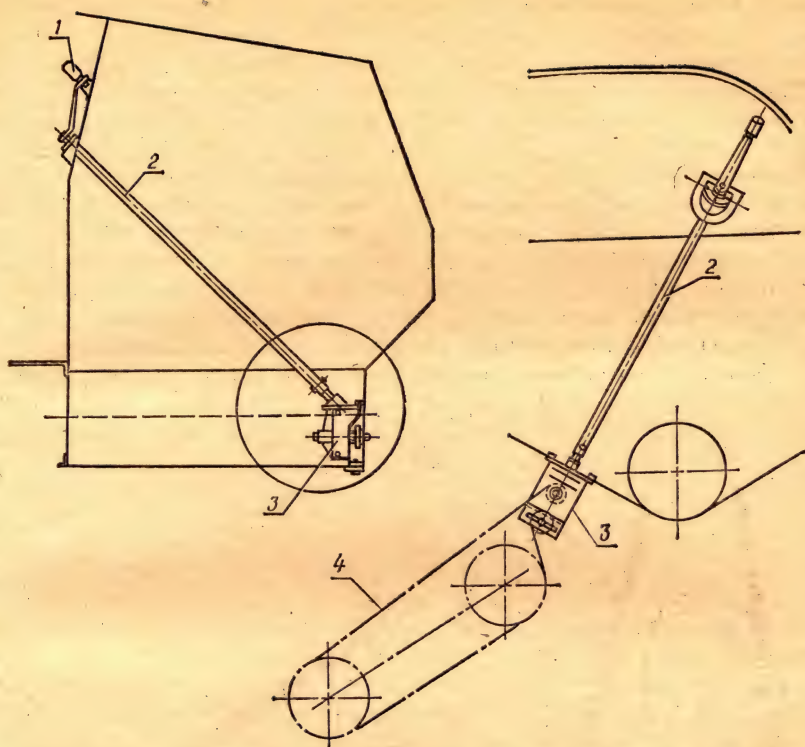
Механизм управления оборотами барабана комбайна СК-6:
